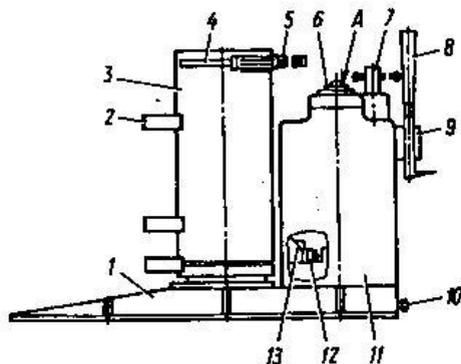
Домкрат ДПГ-10: 1 – основание с поршнем; 2 – лапа; 3 – гидроцилиндр; 4 – ручка для переноски; 5 – пробка для удаления воздуха; 6 – пробка для залива масла; 7 – перепускной клапан; 8 – рукоять насоса; 9 – вал гидронасоса; 10 – пробка для слива масла; 11 – масляный бачок; 12 – магнит; 13 – сетчатый фильтр; А – срезать перед вводом в эксплуатацию
